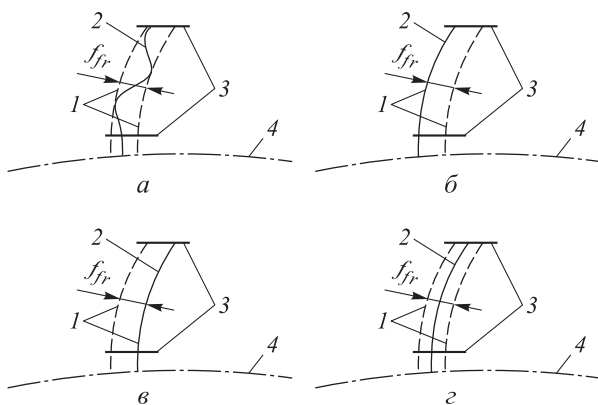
Расположение действительного торцового активного профиля в пределах поля допуска f_f :
